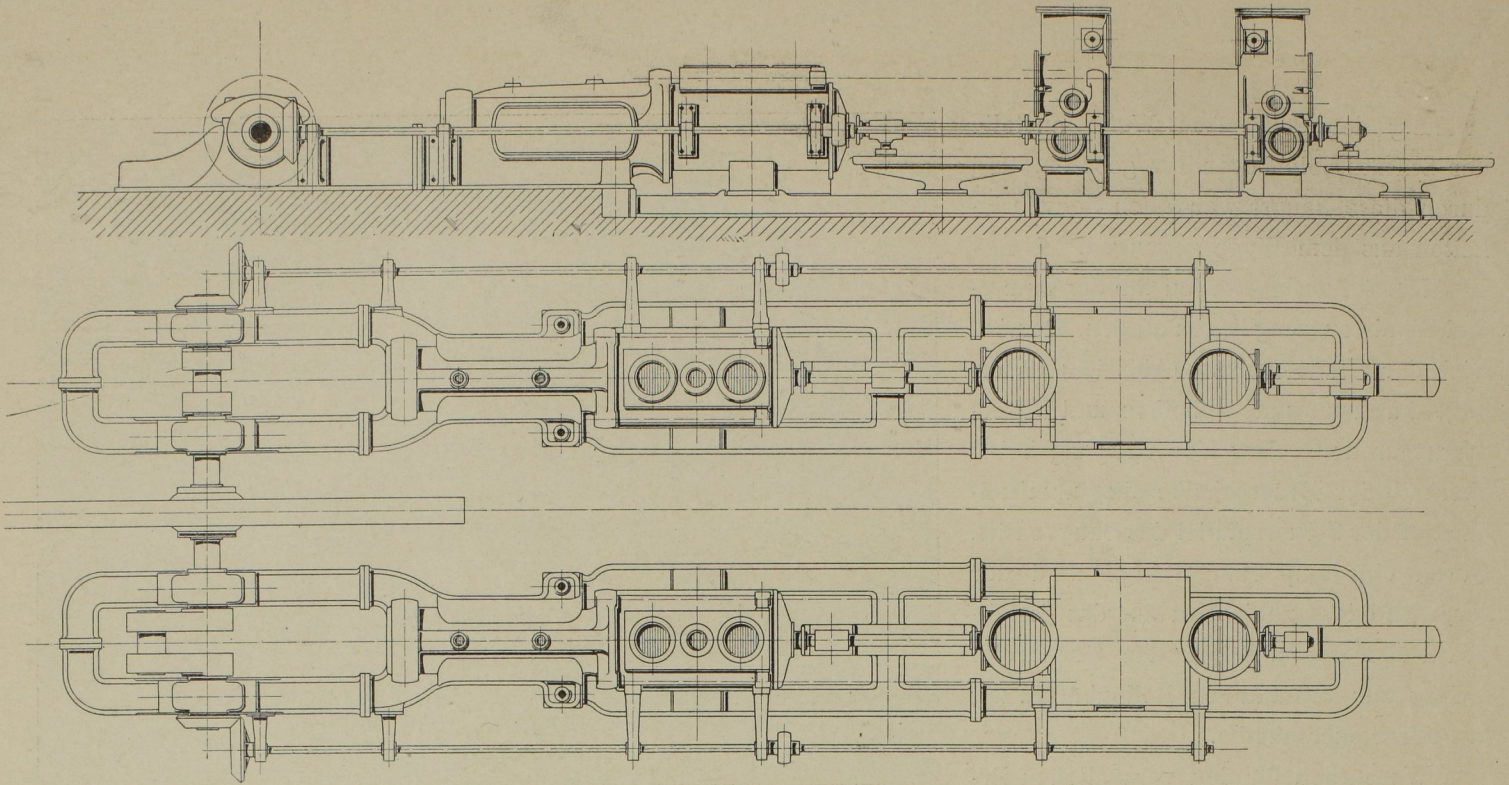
Seitenansicht und Grundriss der Gebläsemaschine. Masst. 1:125.
